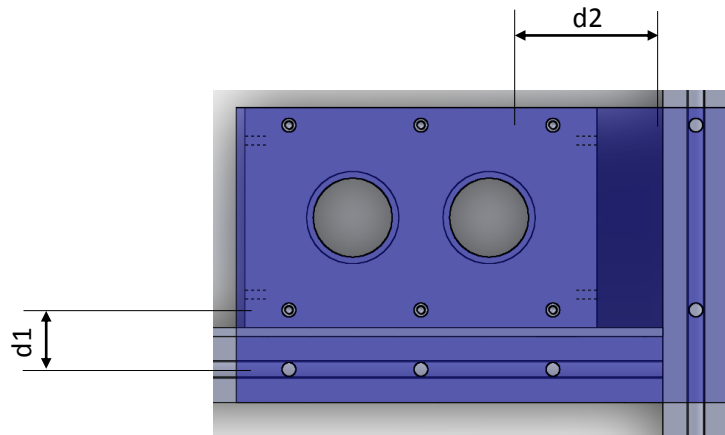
14: Imagen explicativa de las dimensiones de la tapa externa frontal.
